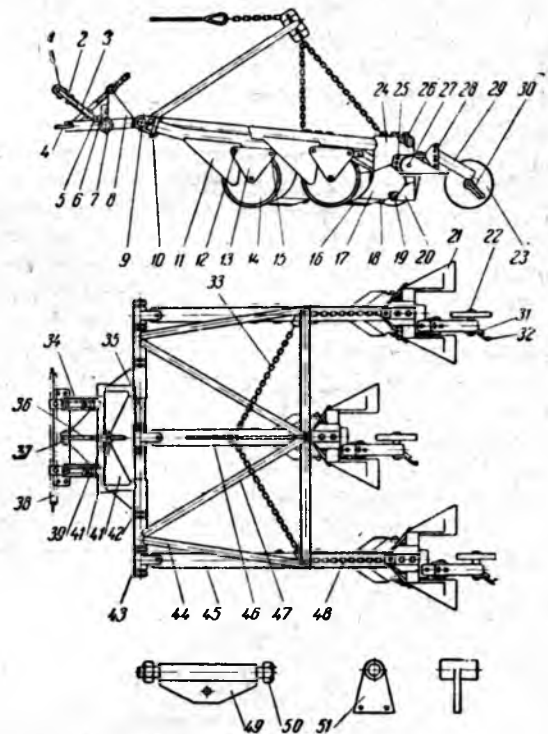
Схема конструкции плуга ПЛН-3-30 с сеялками.
